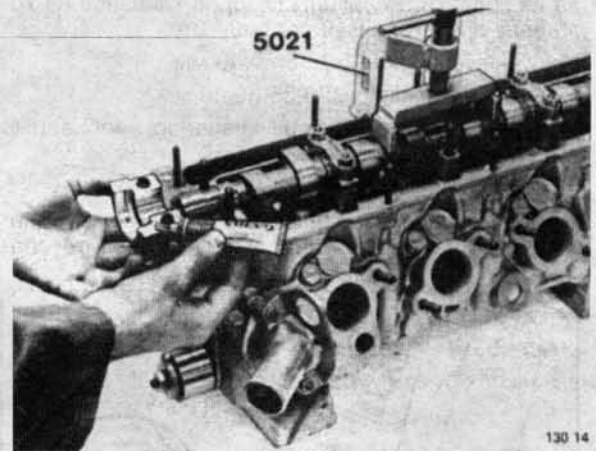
Уплотнение крышки 1-го подшипника распредвала двигателя В19
